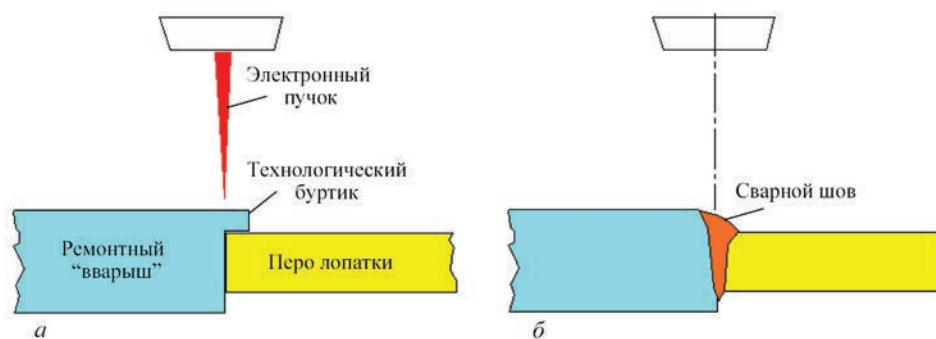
Схема ремонтного ЭЛС-соединения «вварыша» и пера лопатки: а — до сварки; б — после
